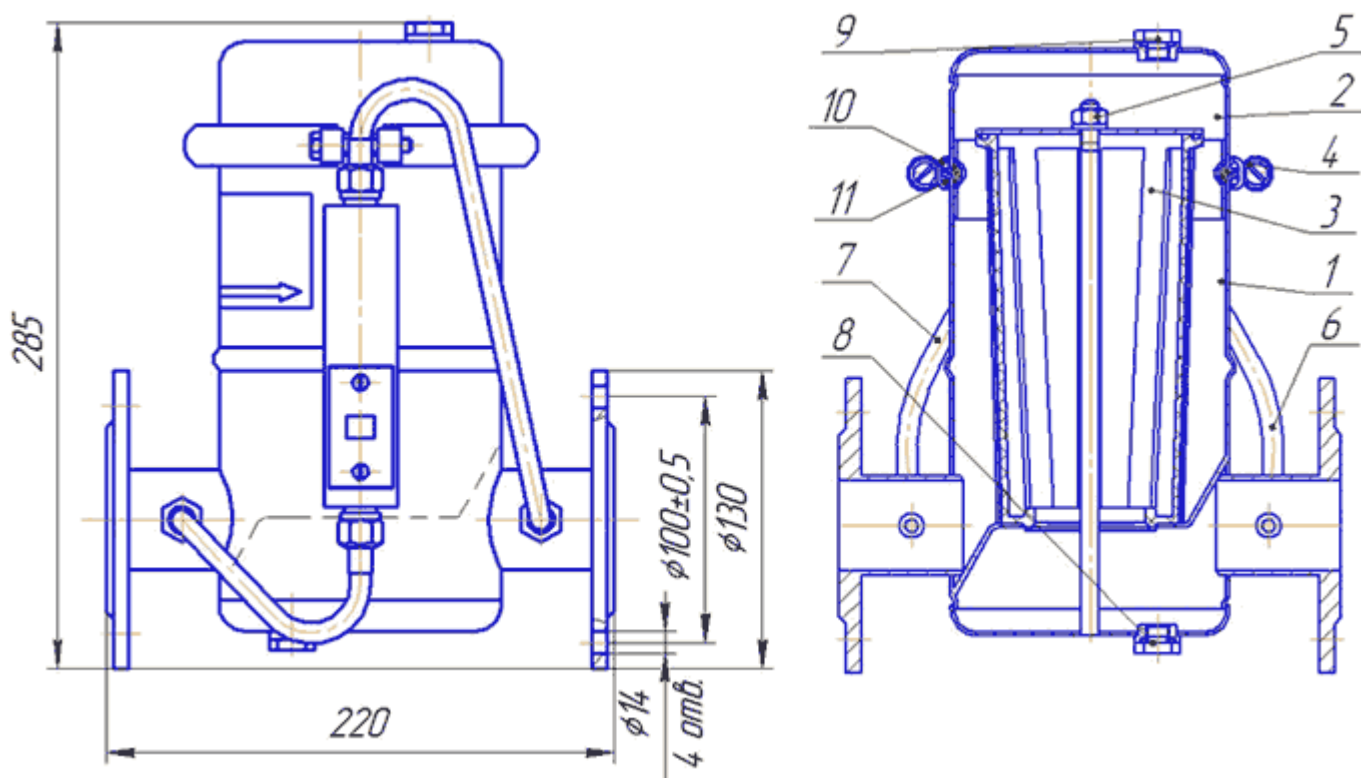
(1 - корпус; 2 - крышка; 3 - фильтрующий элемент; 4 - болт; 5 - гайка; 6 - трубка передачи давления на выходе из фильтра; 7 - трубка передачи давления на входе в фильтр; 8 - сливная пробка; 9 - пробка для удаления воздуха; 10 - хомут; 11 - кольцо уплотнительное.)
